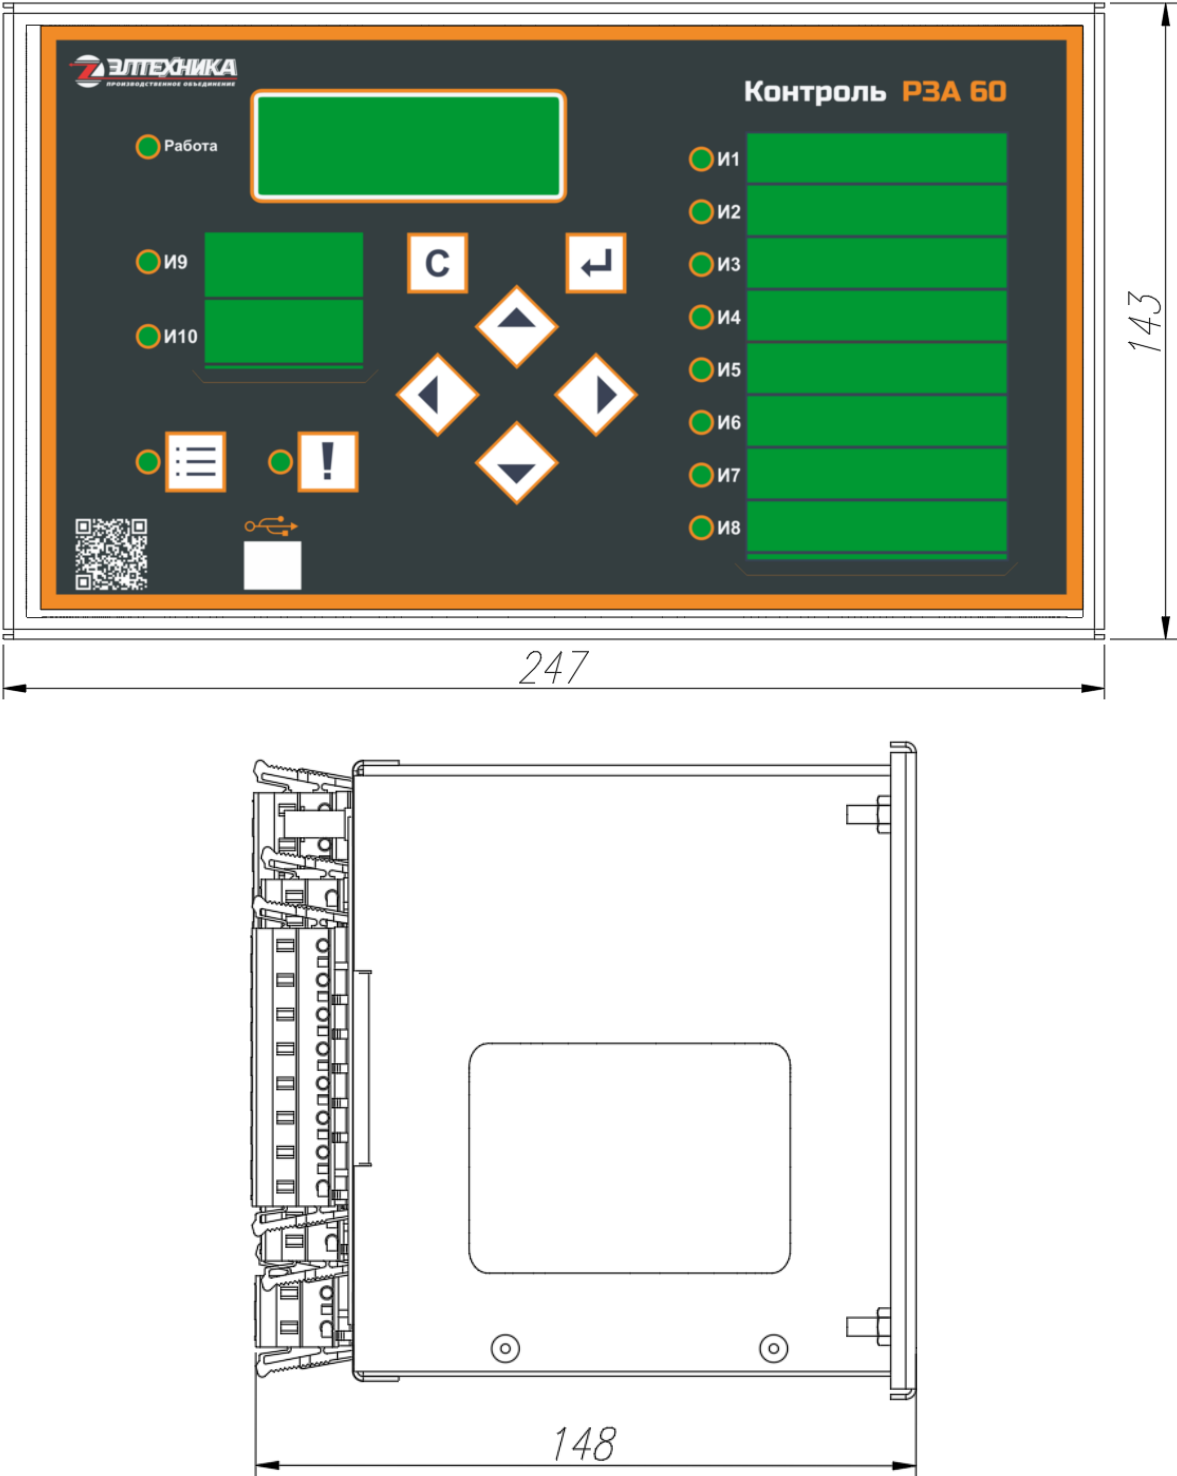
Габаритные размеры Контроль РЗА 60
